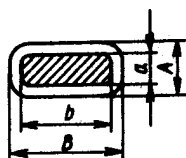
Схема обмоточного провода прямоугольного сечения
